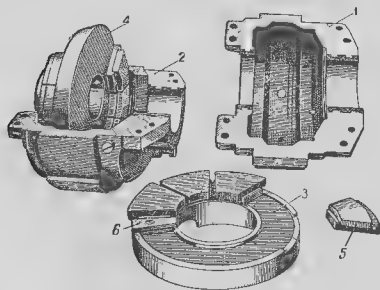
Общий вид разобранного сегментного упорного подшипника.
